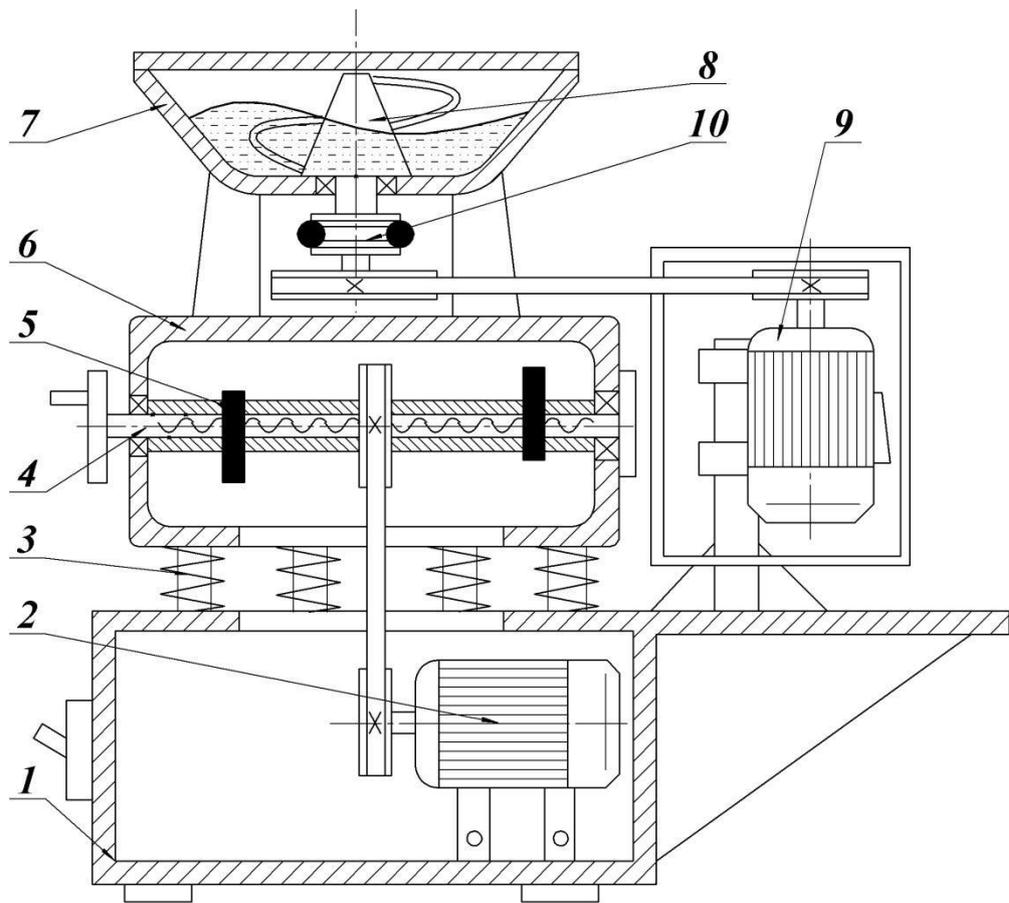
Принципова схема установки для віброабразивної обробки з вертикальним положенням активного робочого органу
